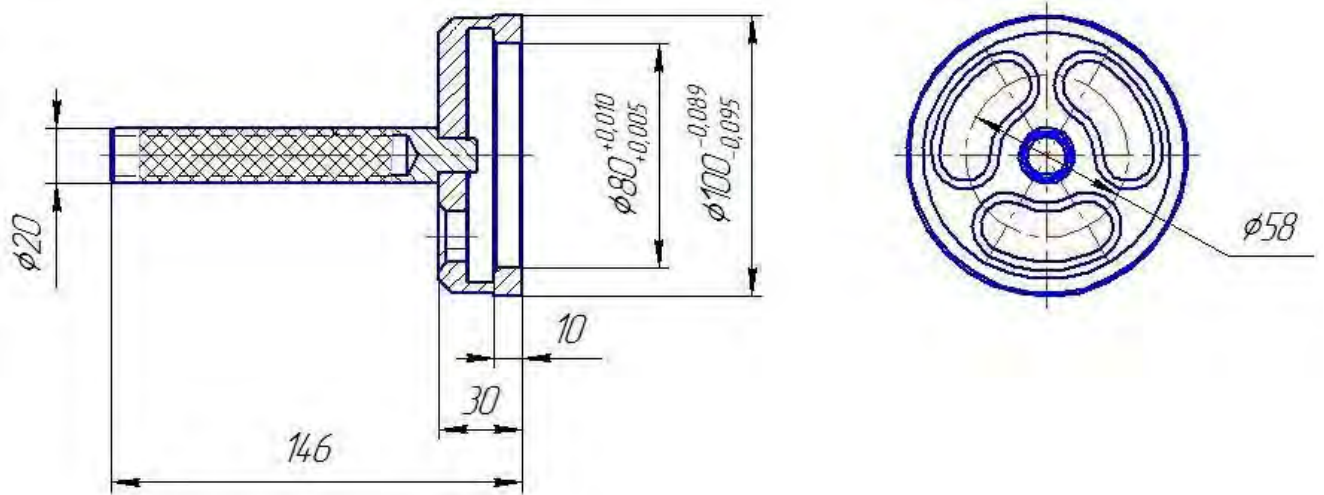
3M 7853-4418, Dorn zum Zentrieren des hinteren Wellendichtrings, komplett mit Stopfbuchshalter relativ zum hinteren Flansch der Kurbelwelle
